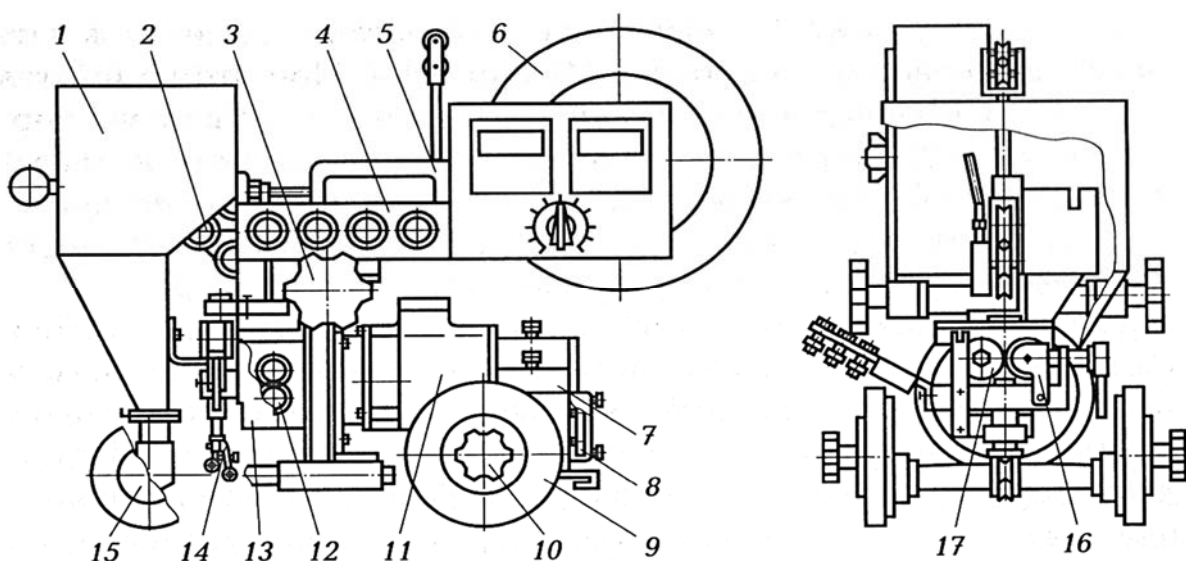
Сварочный трактор КА 001
